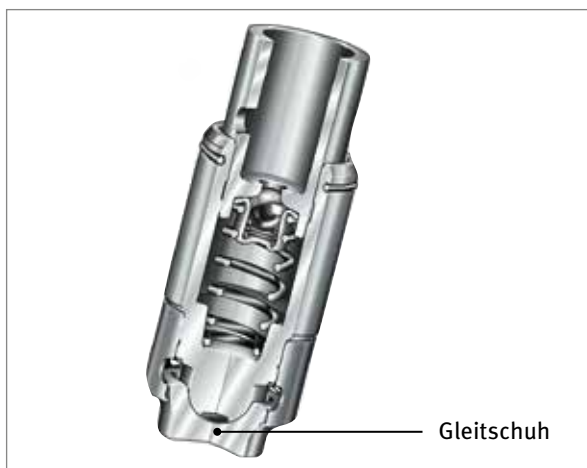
Hydraulisches Einsteckelement mit Gleitschuh
